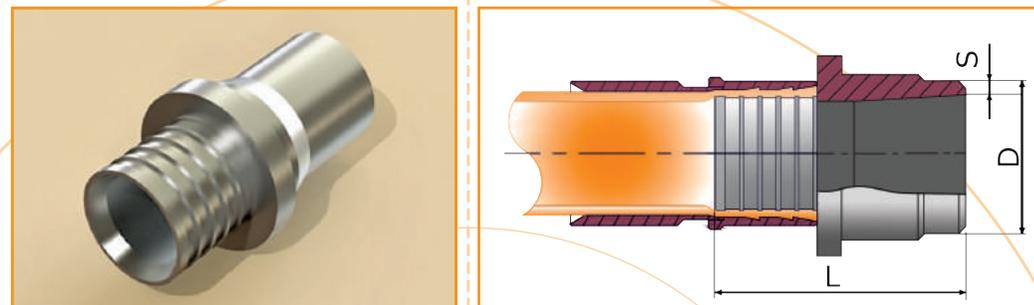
Пресс-фитинг под сварку Тип 2
